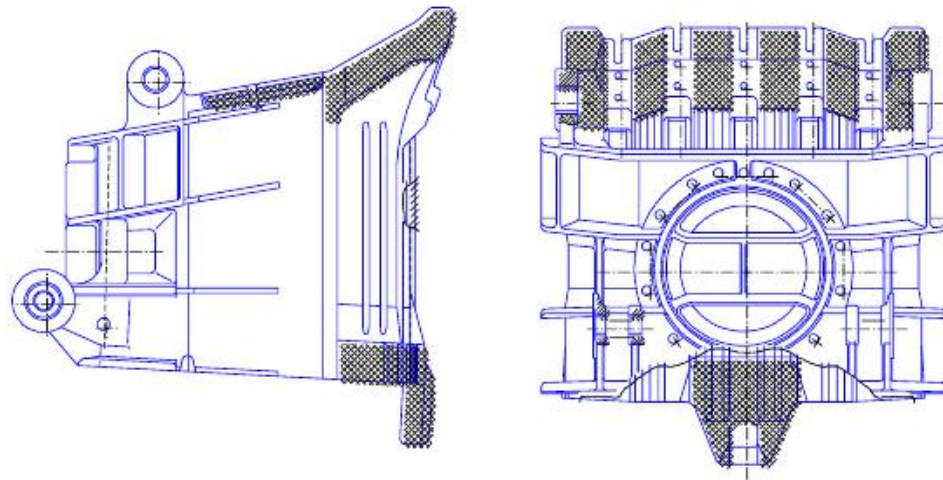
Корпус ковша экскаватора ЭКГ-10
